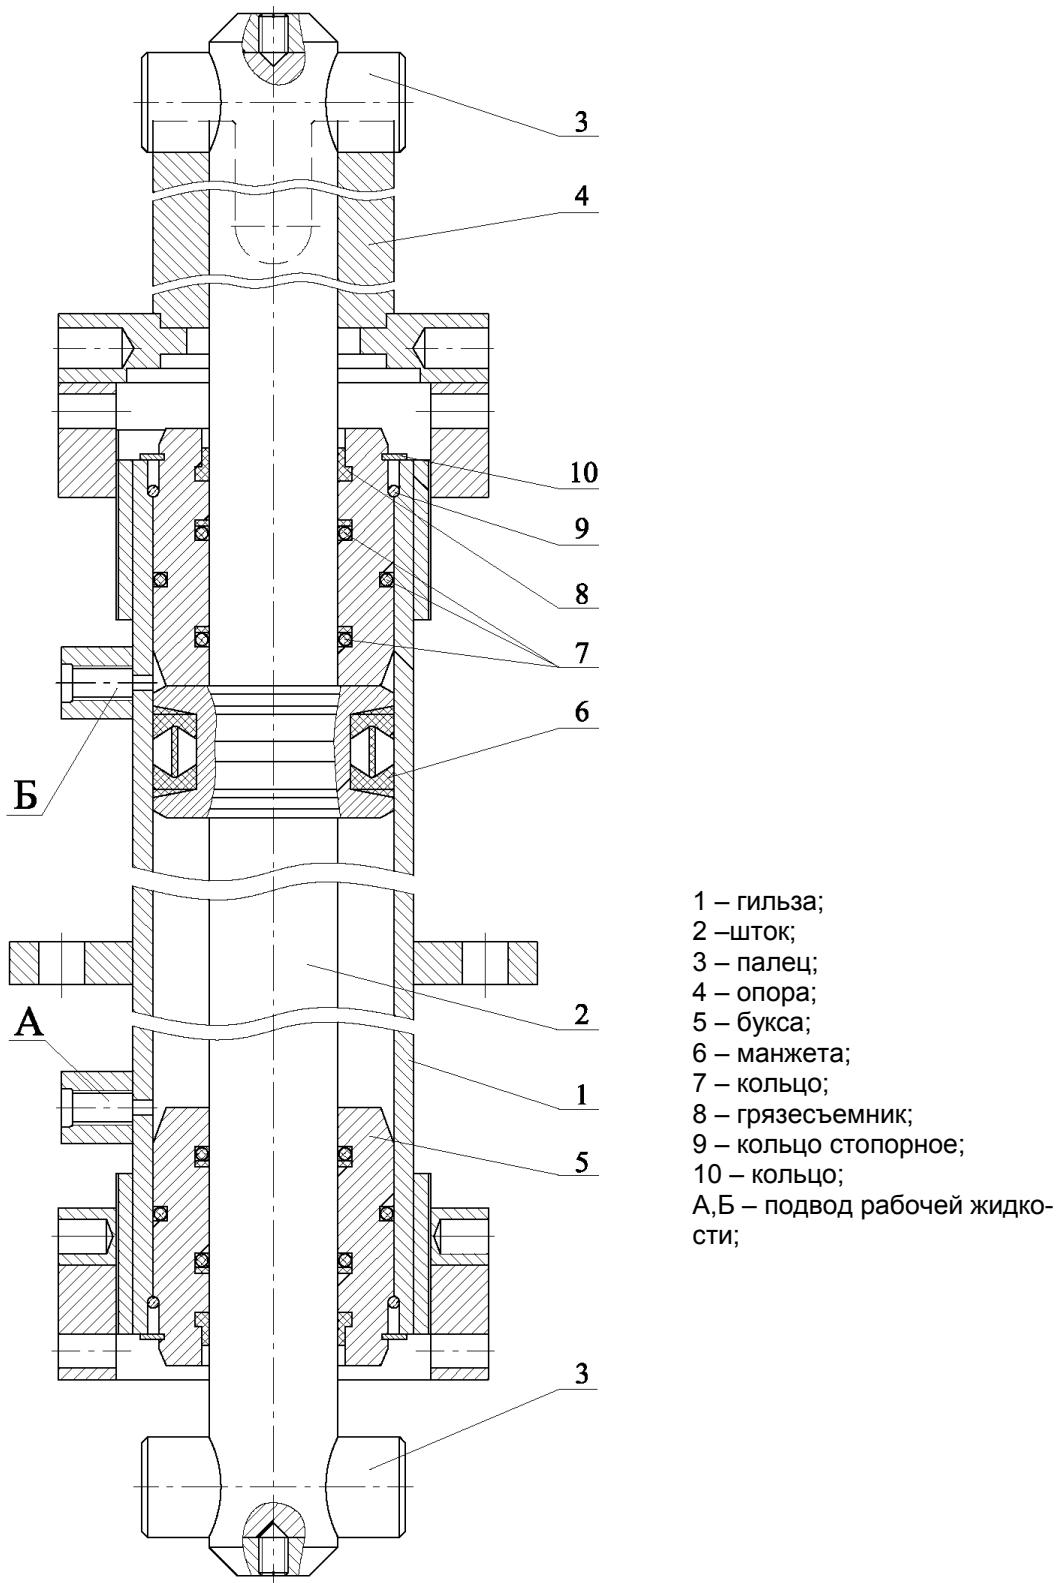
Гидроцилиндр установки дополнительных противовесов
